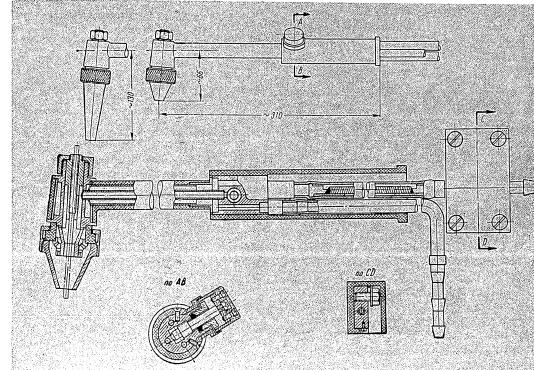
Сварочная горелка среднего габарита для ручной сварки в среде аргона
